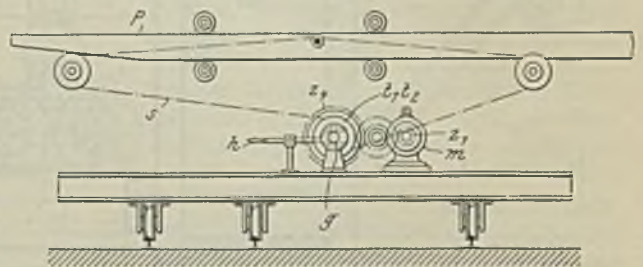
Planiervorrichtung der Maschinenbauanstalt Altenessen mit Seilantrieb.
